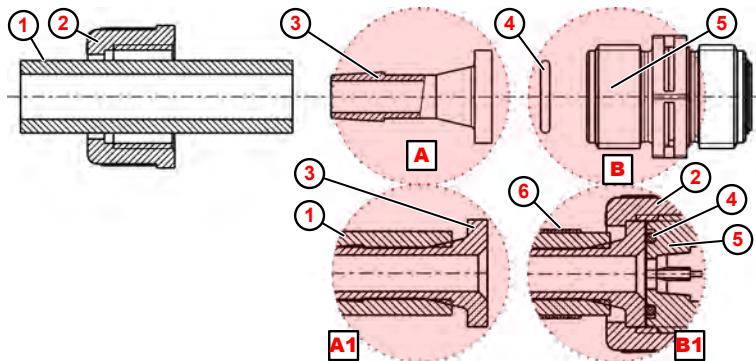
Rohr- und Schlauchanschluss mit Aufstecknippel und Schlauchschielle
